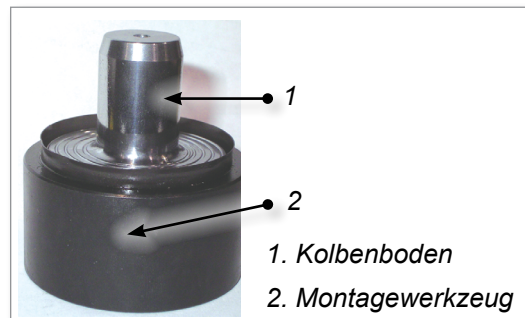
Kolbenboden mit Montagewerkzeug
